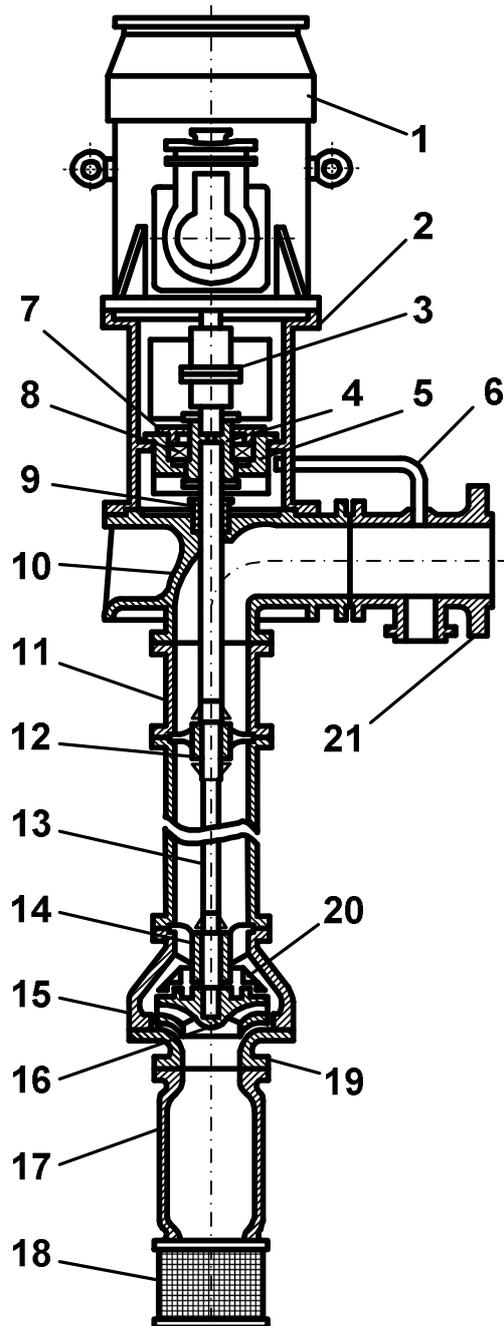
Конструкция насоса ВП-340: 1 – электродвигатель; 2 – проставка; 3 и 4 – цепная и жесткая муфта; 5 – опорный стакан; 6 – трубка; 7 – фланец; 8 – подшипник; 9 – сальник; 10 – колено; 11 – напорный трубопровод; 12 и 14 – верхний и нижний подшипник скольжения; 13 – вал; 15 – корпус; 16 – рабочее колесо; 17 – гибкий всасывающий трубопровод; 18 – приемная сетка; 19 и 21 – всасывающий и напорный патрубки; 20 – обтекатель колеса
